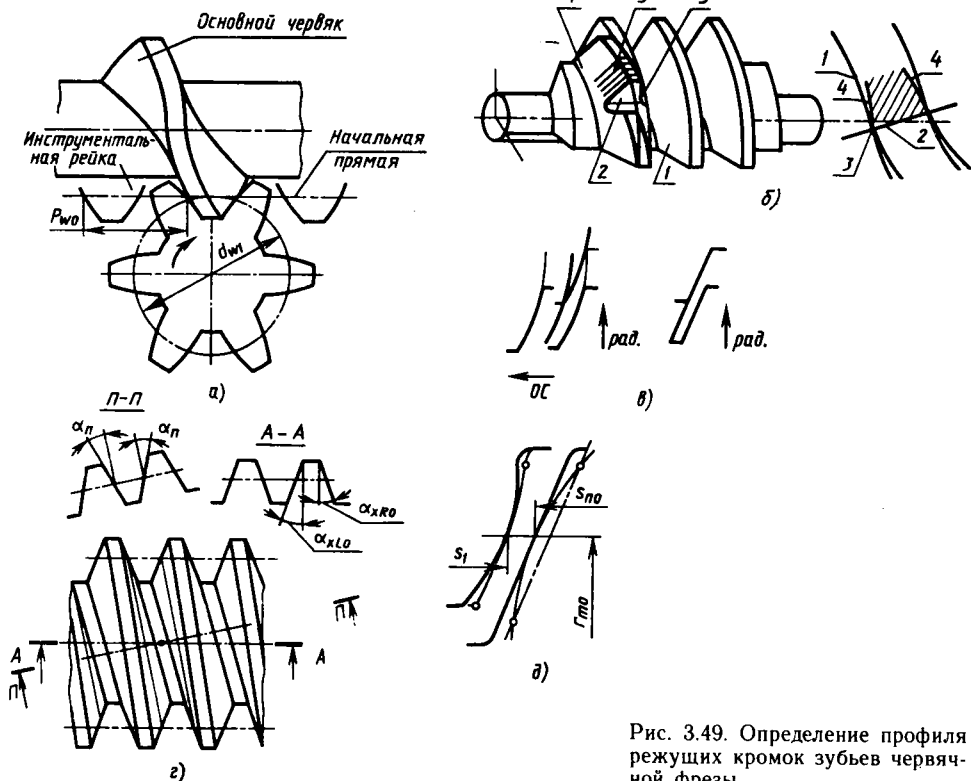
Определение профиля режущих кромок зубьев червячной фрезы
